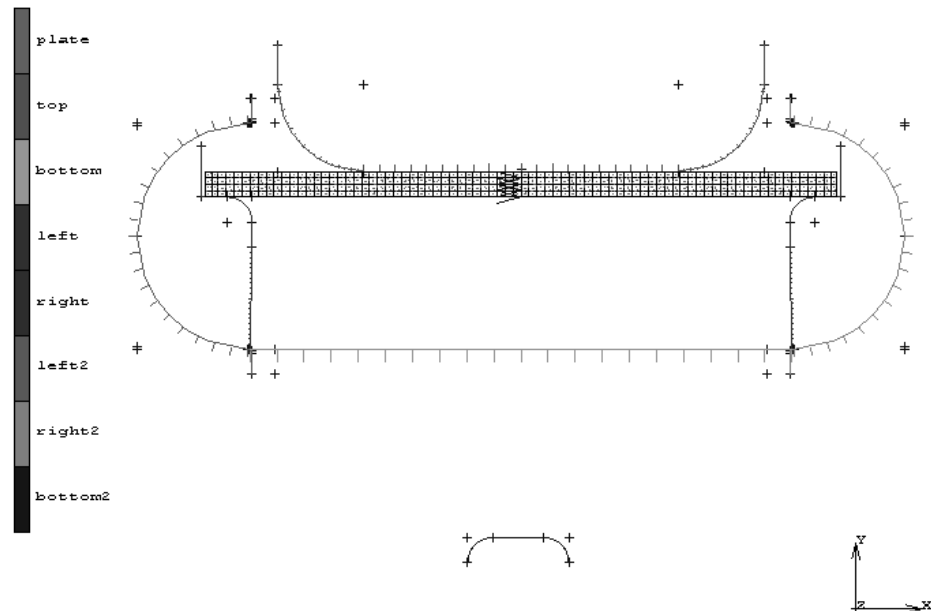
Модель рабочих частей комбинированного штампа для двухугловой гибки и свертки (условно совмещены на плоскости чертежа)
